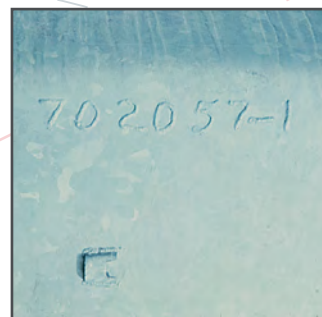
Se pueden usar cordones de soldadura para identificar la fabricación
